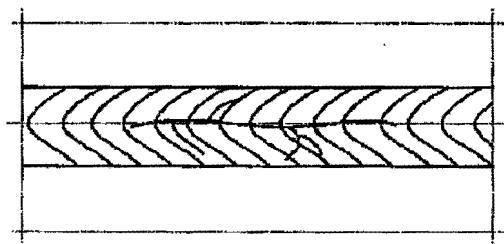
26. Разветвленная трещина сварного соединения
